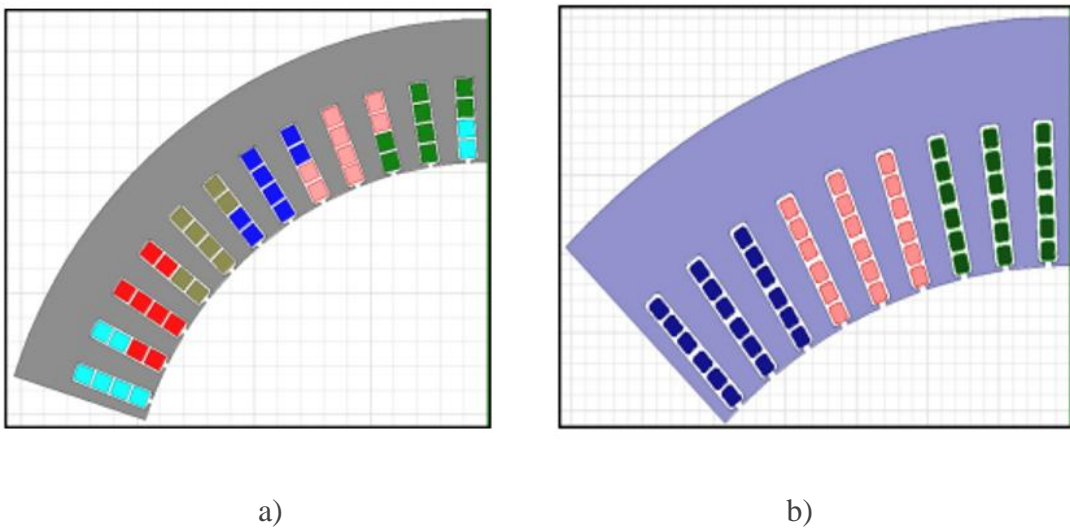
a) stator b) rotor Chevrolet Bolt EV [14].
